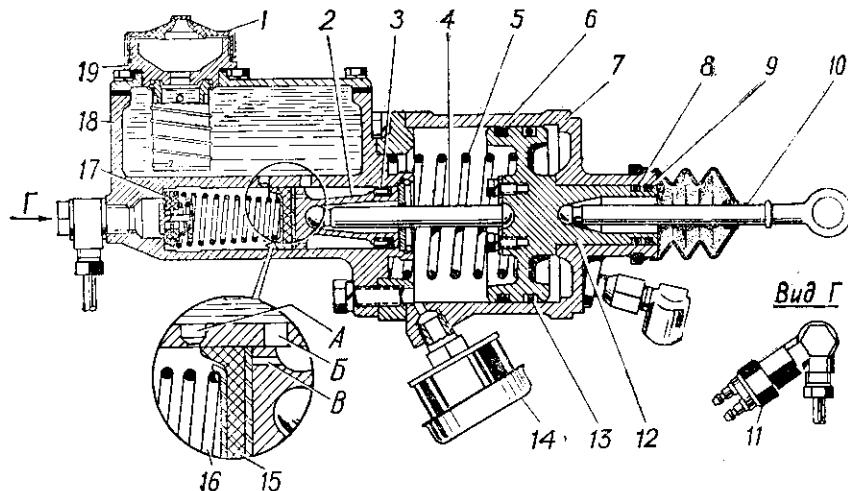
Главный цилиндр и пневмоусилитель тормозного привода:
